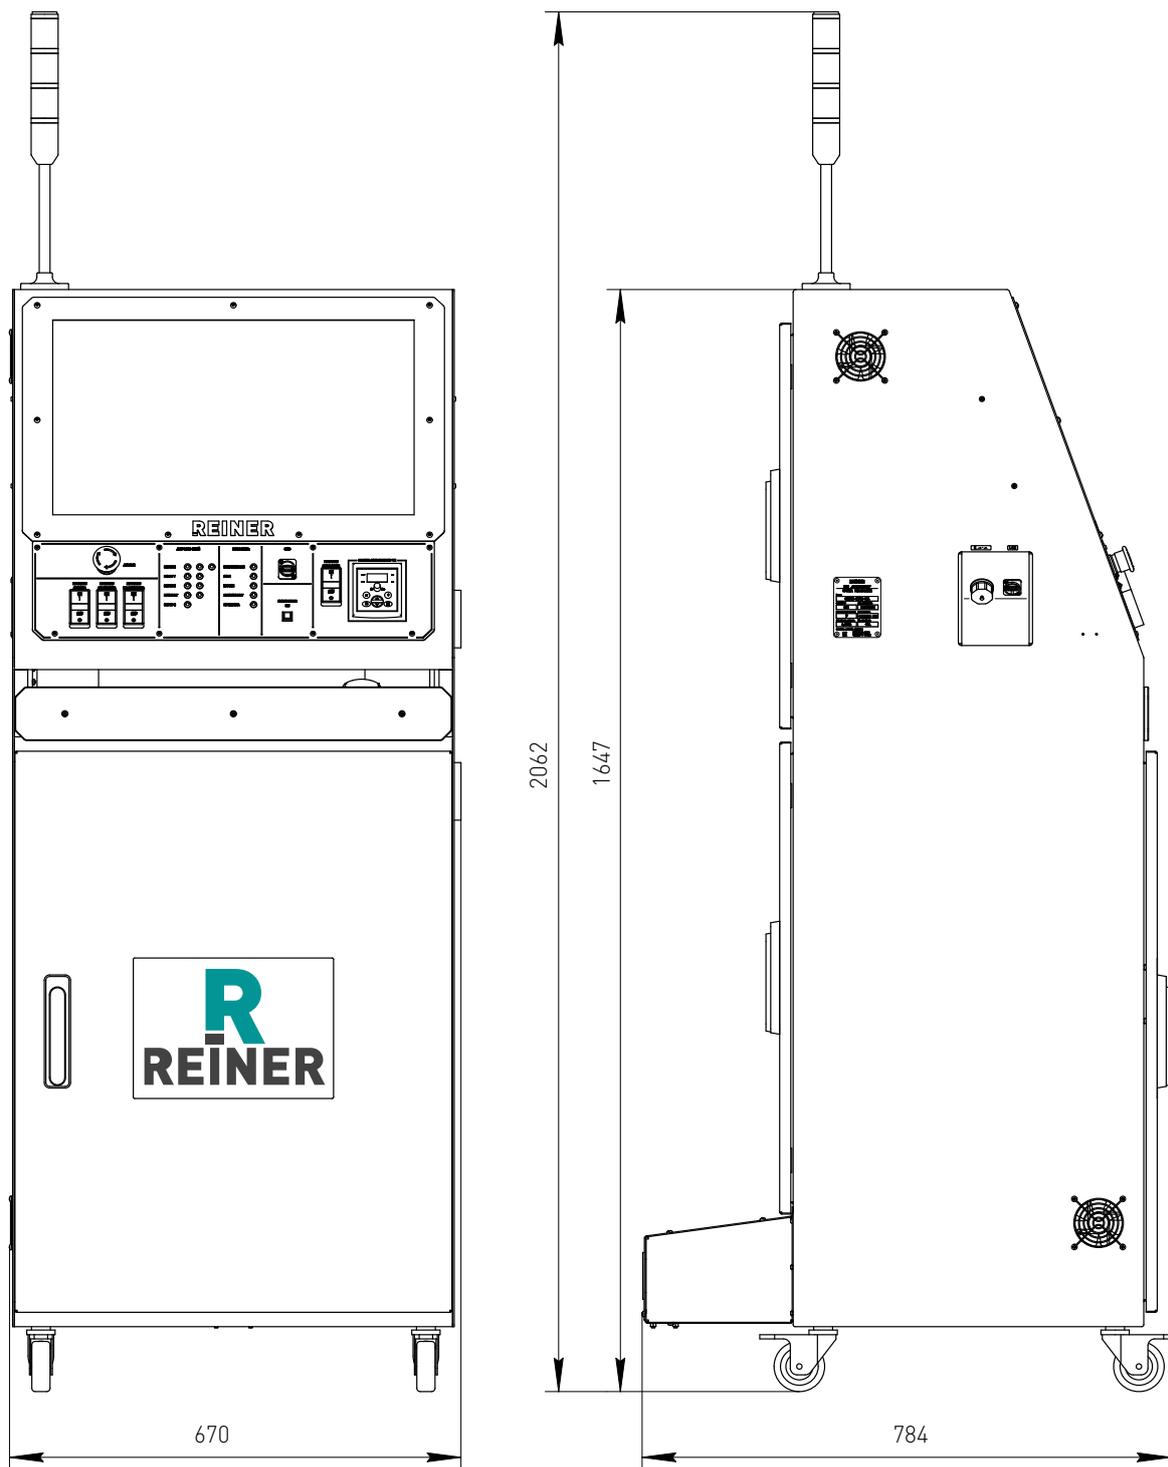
Габаритные размеры фрезерного станка с ЧПУ REINER ME140M.
